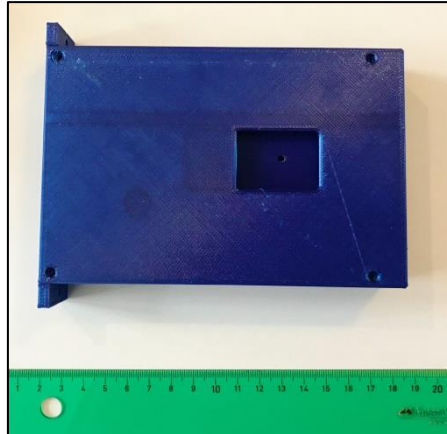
Montaje de la tapa derecha y cierre del conjunto.
